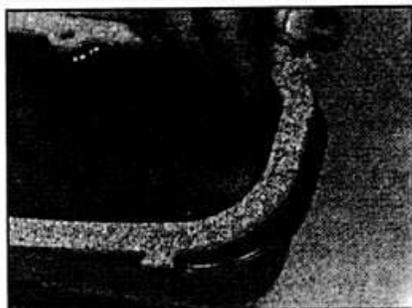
А.4. Установка прокладки крышки в крышку головки блока цилиндров.
